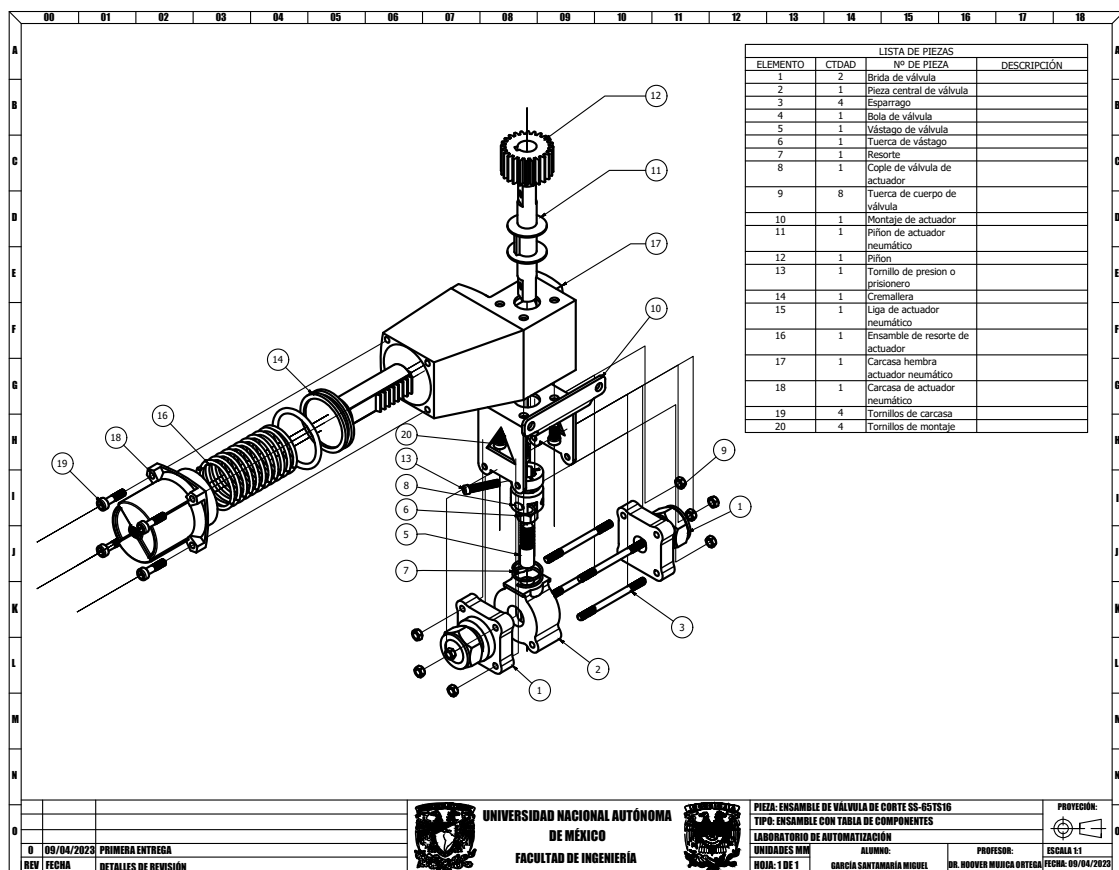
Ensamble explosionado y tabla de componentes de válvula de corte Swagelok SS-65TS16 con actuador neumático
